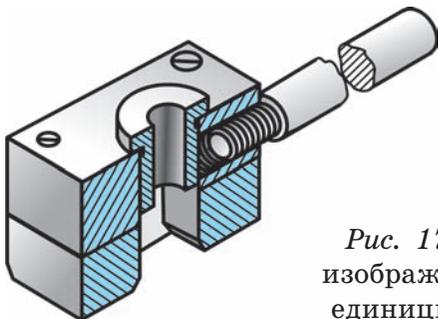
Наглядное изображение сборочной единицы «кондуктор»
